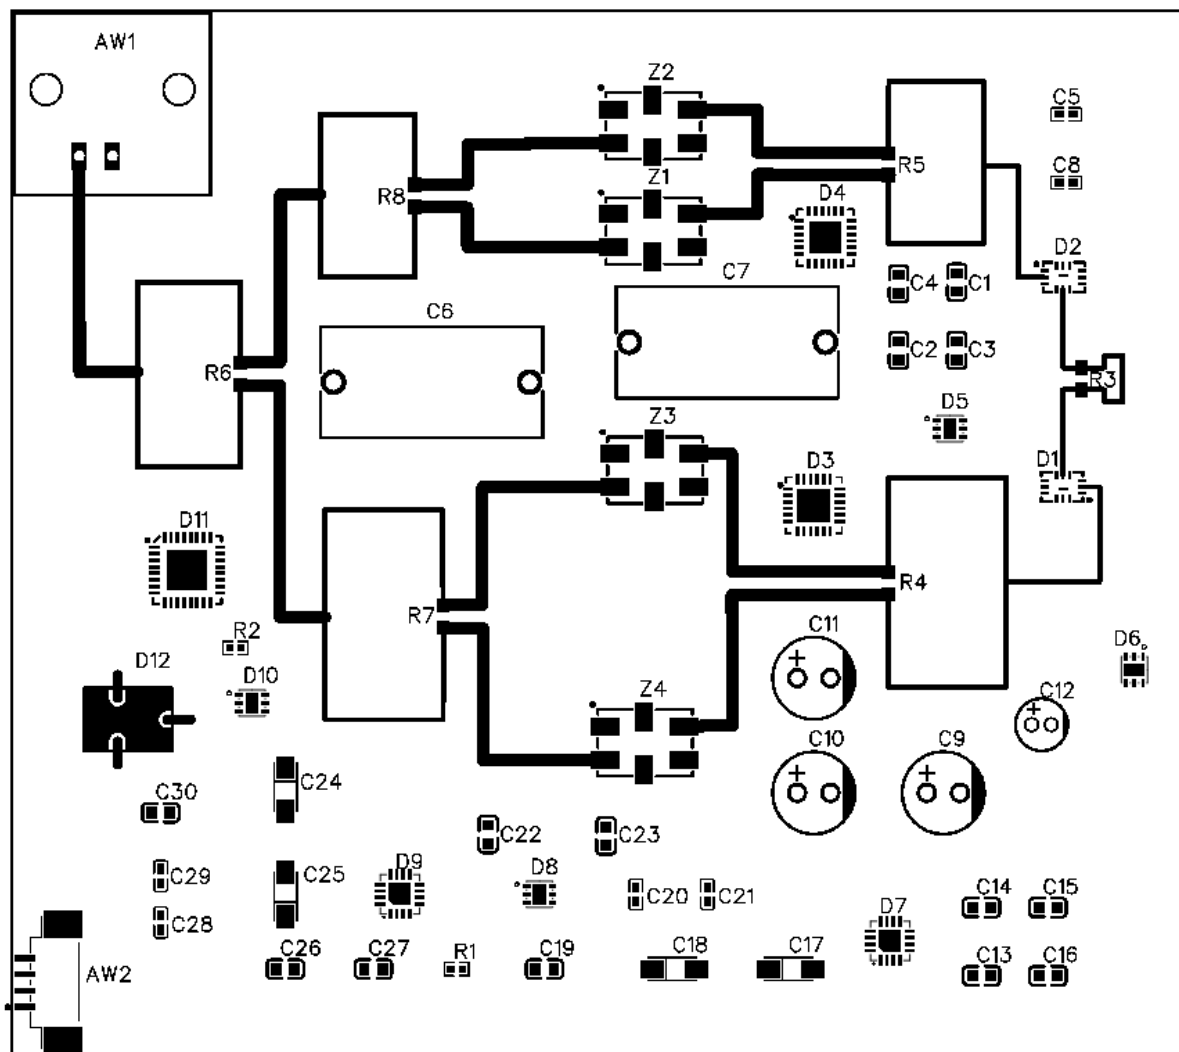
Сборочный чертеж платы печатной ретранслятора
